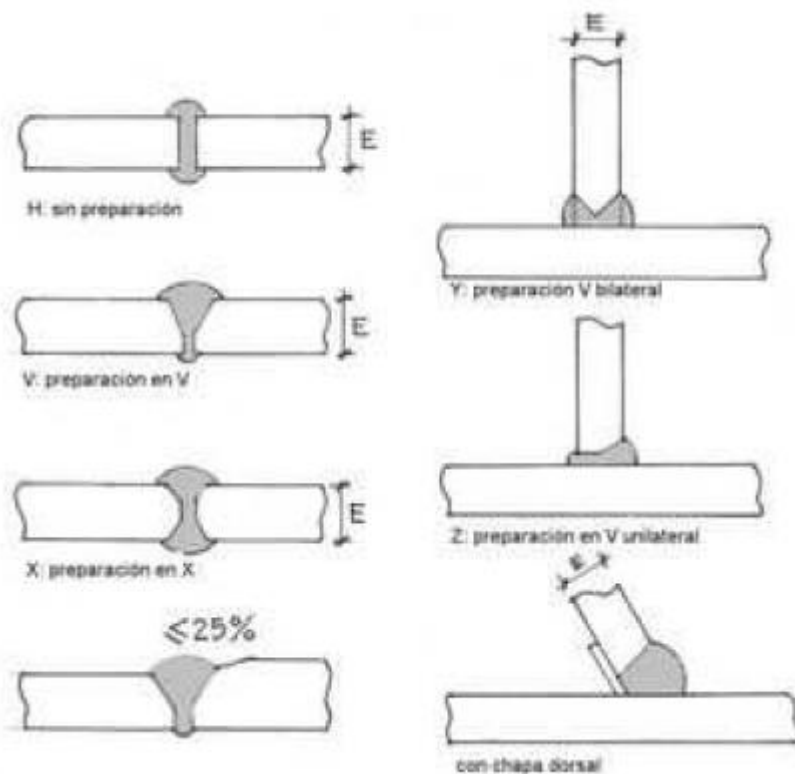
Tipos de soldaduras “a tope”.
